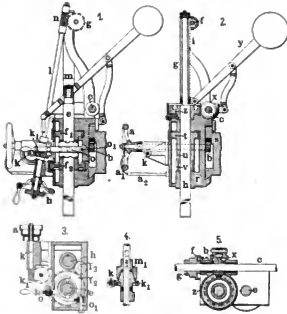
Z. A.: Radiol-Bohr- und Gewindeschneid-Maschine.
